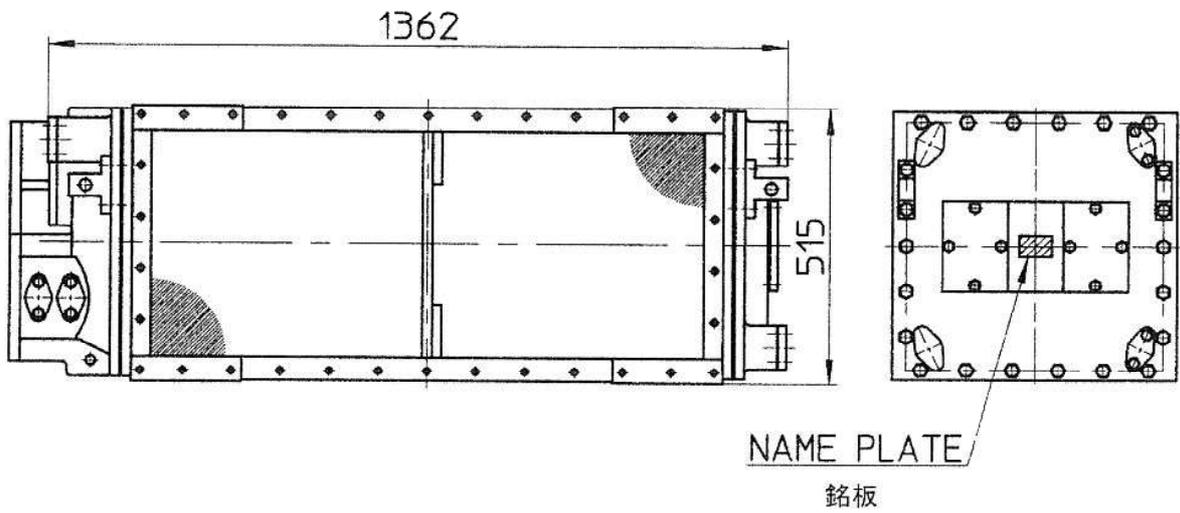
空気冷却器 Air cooler 形式 TYPE ;AHK177S
